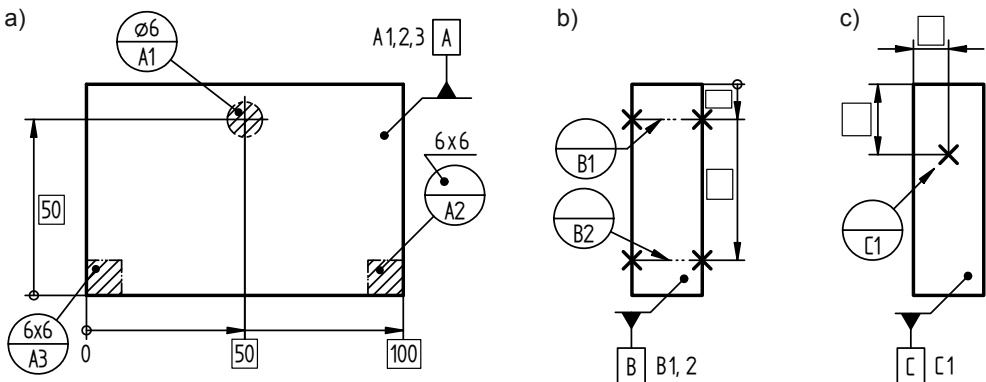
Möglichkeiten zur Bezugsstellenangabe. a) Flächenauflage an 3 Bezugsstellen, b) Linienauflage an 2 Linien, c) Punktauflage an 1 Punkt
